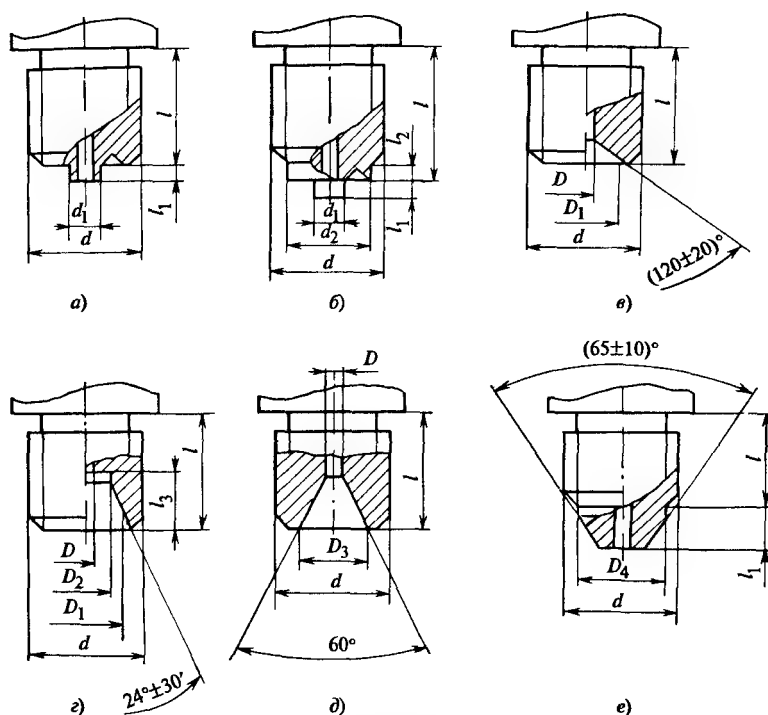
Варианты изготовления присоединительного штуцера:
